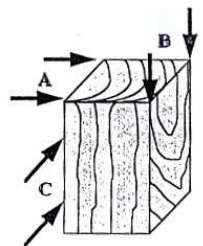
Les trois modes de coupe A, B et C d'après Kivimaa [1]
